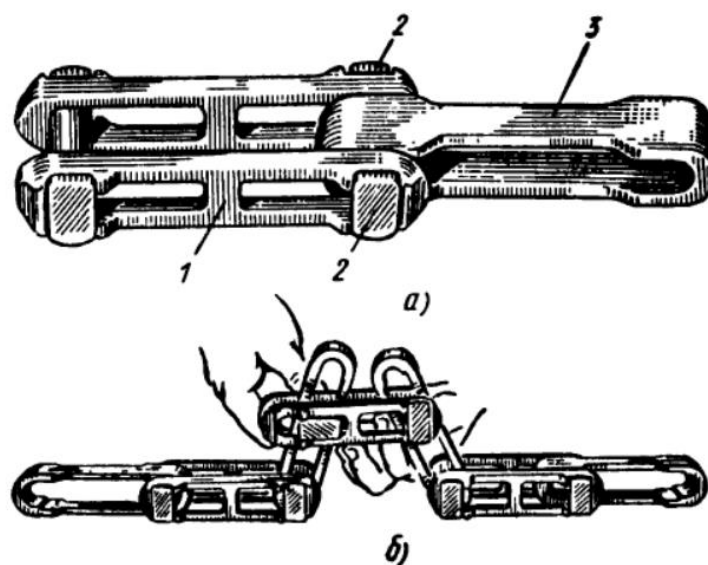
Горячештампований розбірний ланцюг а – загальний вигляд; б – процес розбірки
